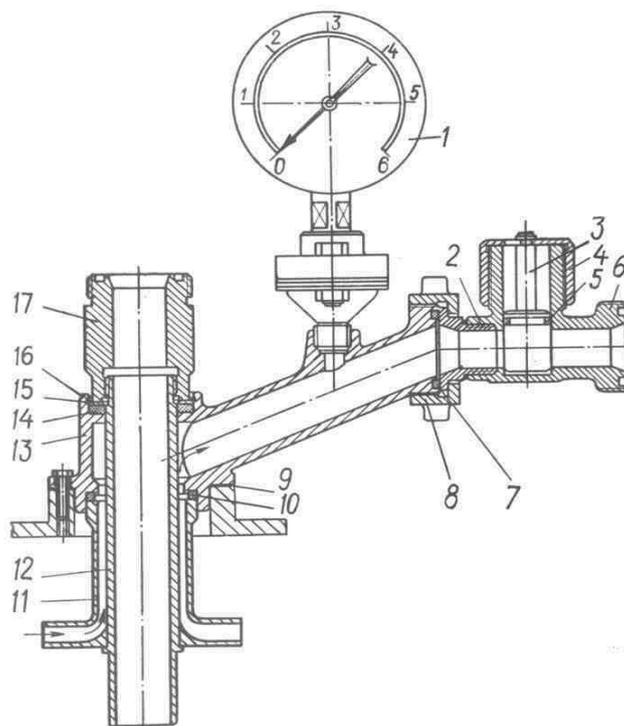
Приемно-отводящее устройство сепаратора ОМА-3М: 1 – манометр; 2 – штуцер; 3 – поршень; 4 – регулировочная гайка; 5, 7, 10, 14 – уплотнительные кольца; 6 – корпус; 8 – накидная гайка; 9 – регулировочные прокладки; 11 – диск напора молока; 12 – центральная трубка; 13 – корпус приемника; 15 – шайба; 16 – кольцо; 17 – втулка
